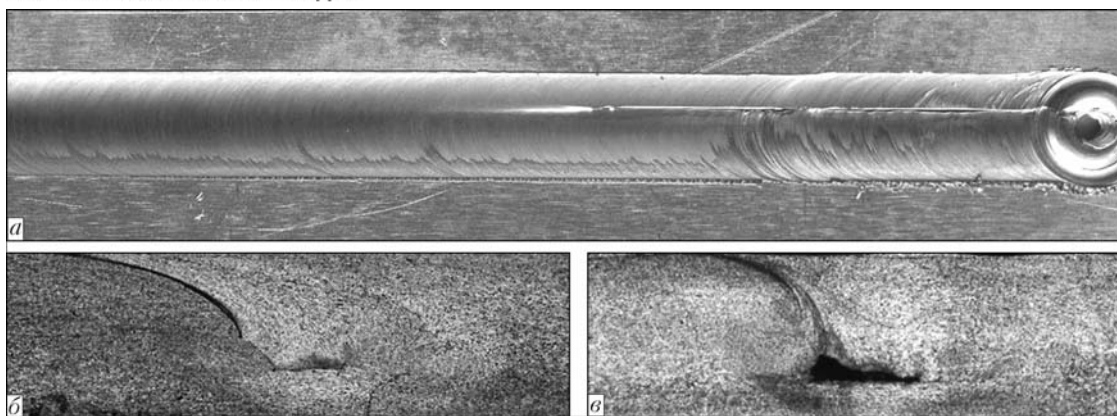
Внешний вид лицевой поверхности шва (а, $\times 1,4$), полученного СТП при сборке стыка с переменным зазором (0,2...1,2 мм) между кромками, и поперечные макрошлифы сварных соединений сплава АМг2 толщиной 2 мм при зазоре 0,3 (б) и 0,5 мм (в)
